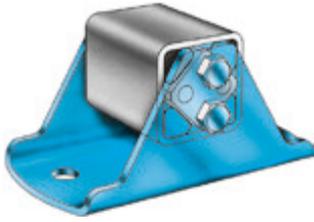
Innenvierkant mit durchgehenden Bohrungen und Support UV
